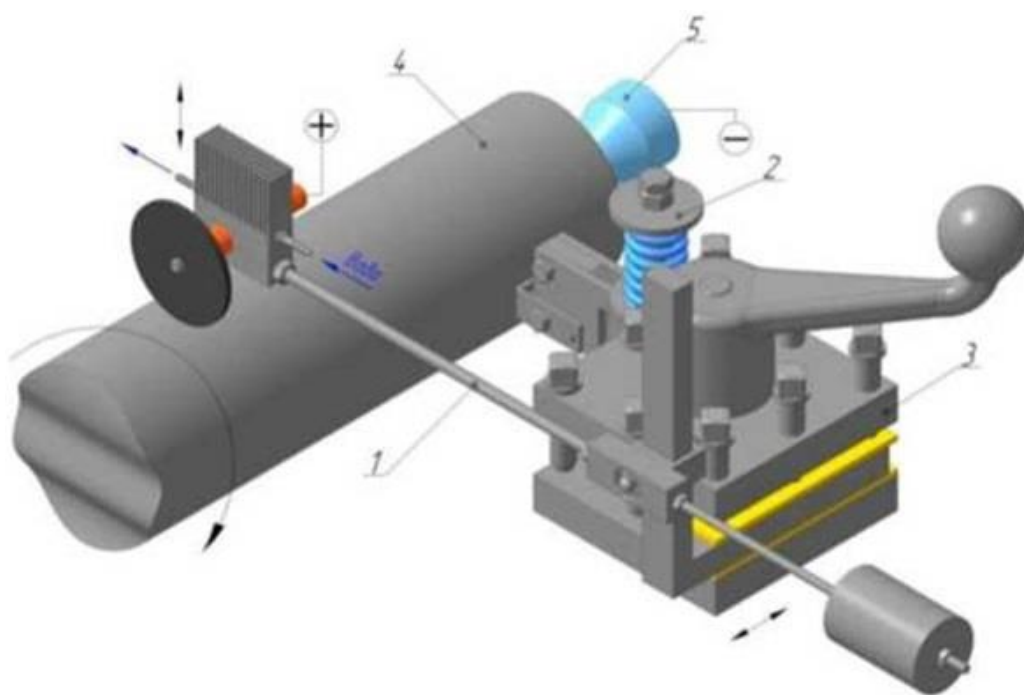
Тривимірна модель-схема установки для формування комбінованого зносостійкого покриття: 1 - пристрій для ЕІЛ; 2 - пристрій для обкочування; 3 - супорт токарно-гвинторізного верстату; 4 - оброблювана деталь; 5 - центр з електричним контактом.
